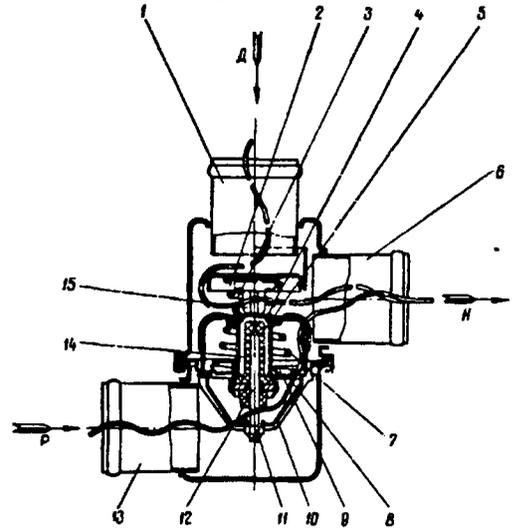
Термостат: 1 - входной патрубок (от двигателя); 2 - перепускной клапан; 3 - пружина перепускного клапана; 4 - стакан; 5 - резиновая вставка; 6 - выходной патрубок; 7 - пружина основного клапана; 8 - седло основного клапана; 9 - основной клапан; 10 - держатель; 11 - регулировочная гайка; 12 - поршень; 13 - входной патрубок от радиатора; 14 - наполнитель; 15 - обойма; D - вход жидкости от двигателя; P - вход жидкости от радиатора; H - выход жидкости к насосу
